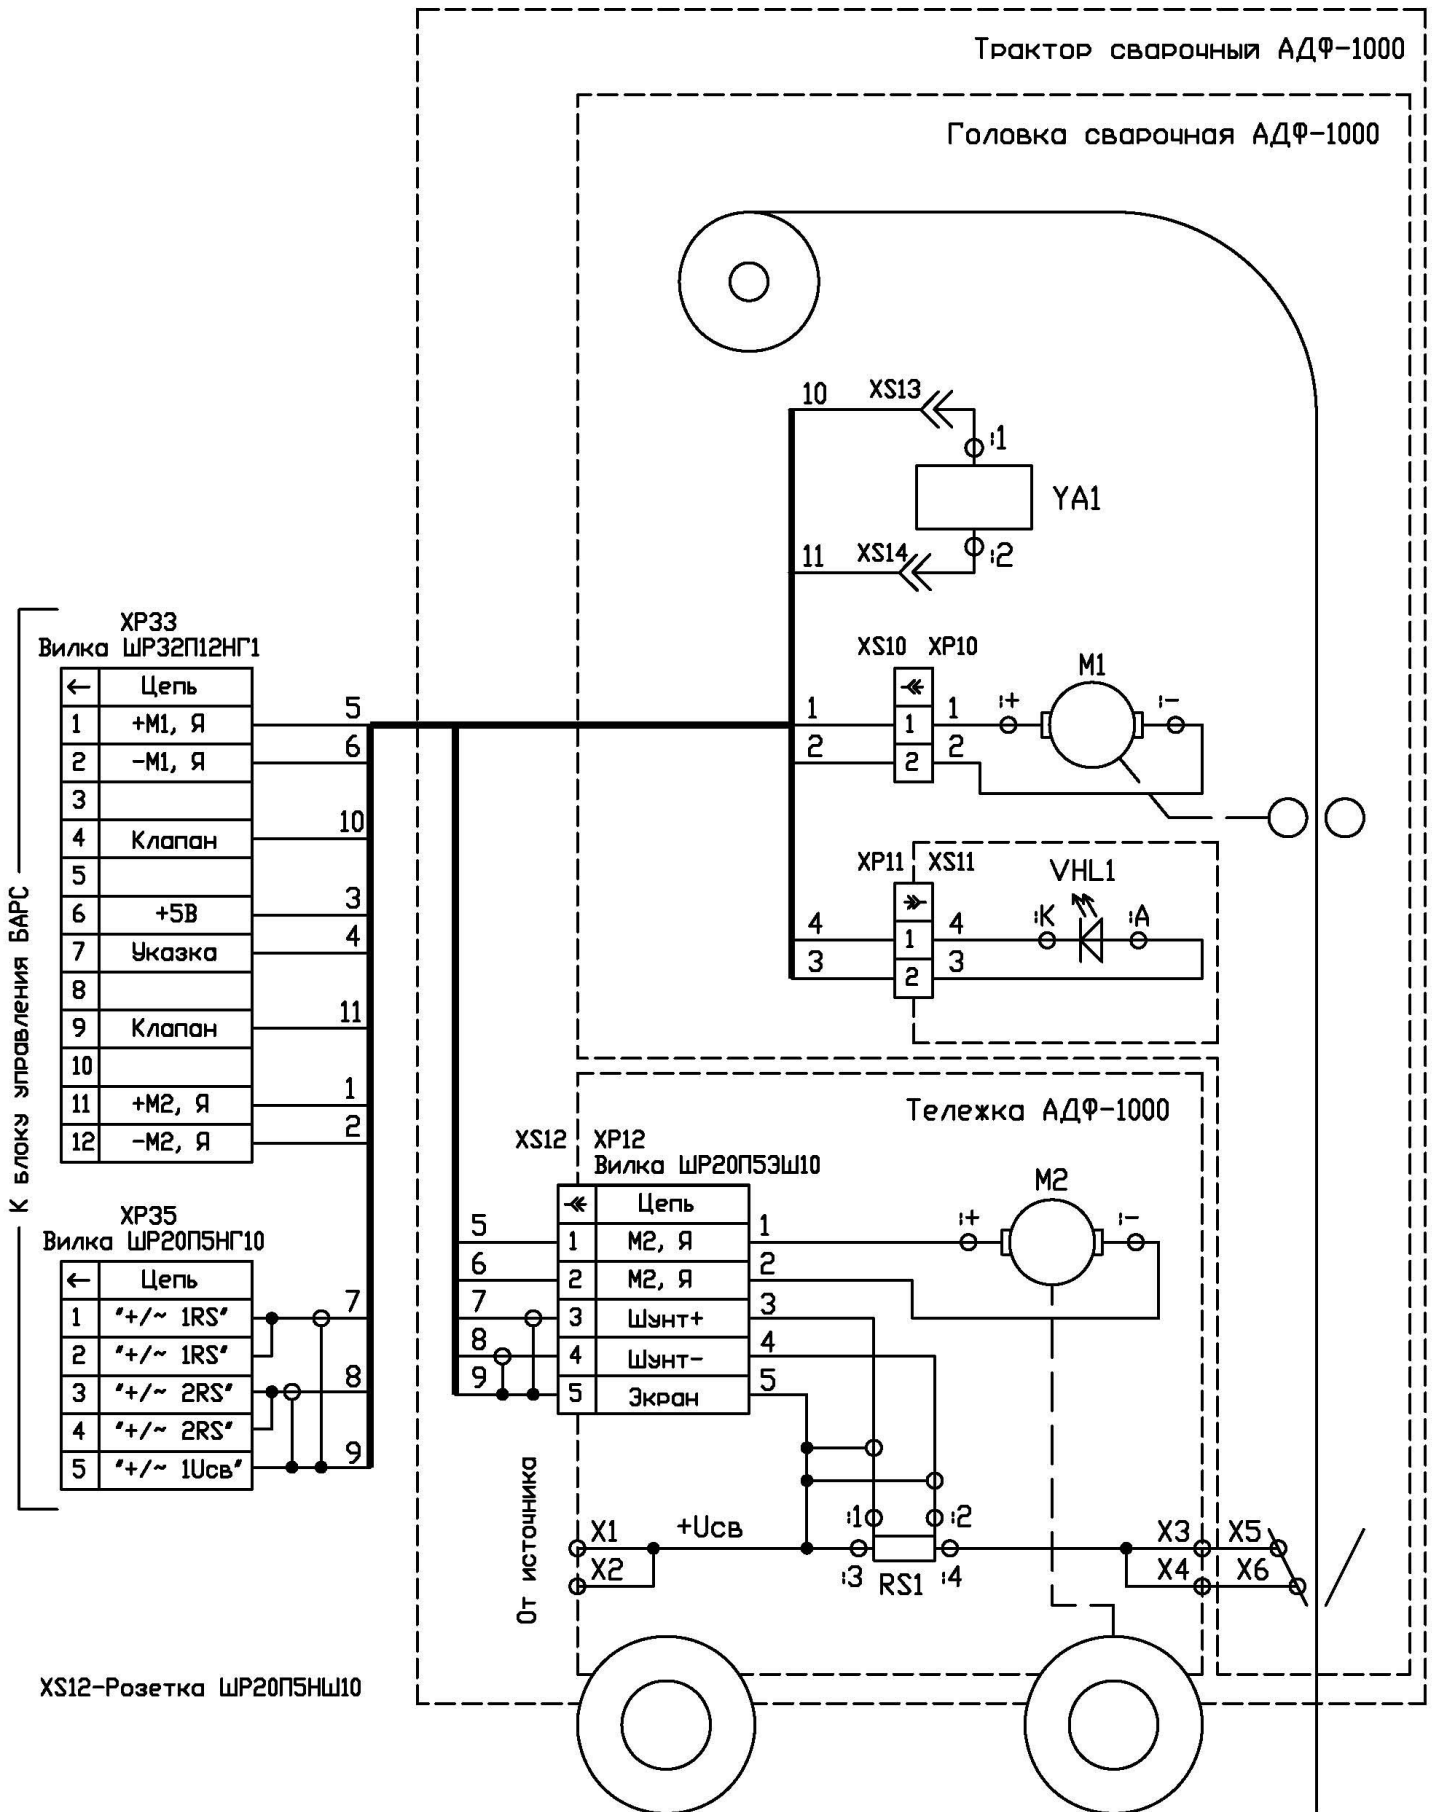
Схема электрическая принципиальная автомата для сварки GMAW, с блоком управления «БАРС».
